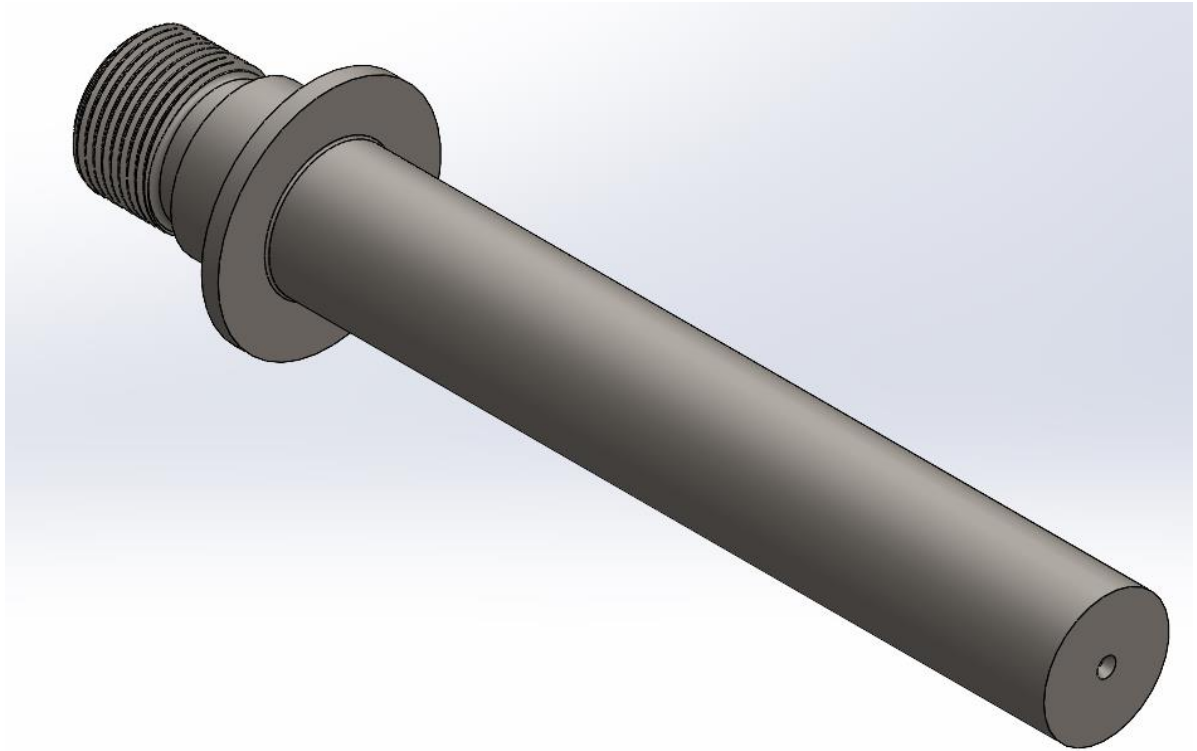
Заготовка для обробки деталі на операції 040
